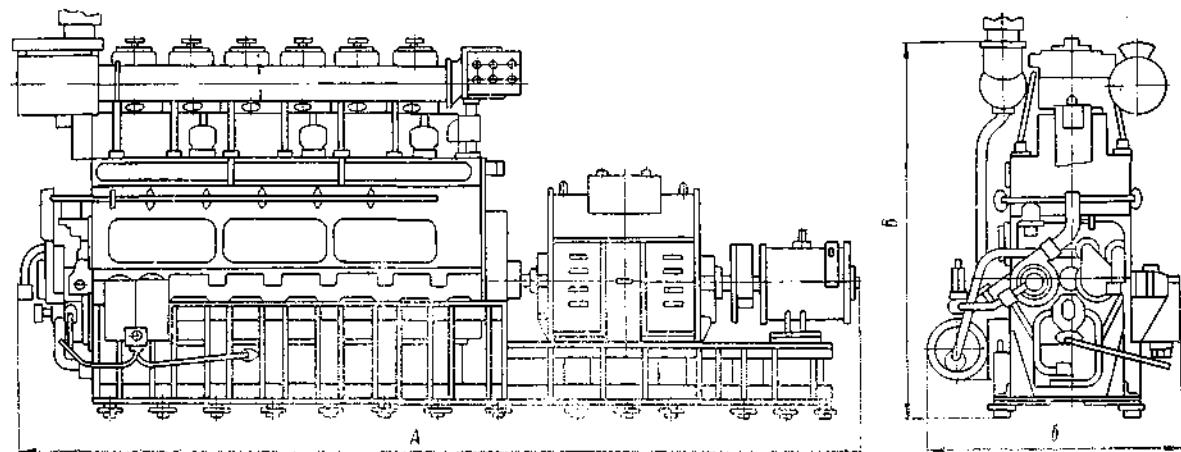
Габаритный чертеж дизеля 6Ч23/30
